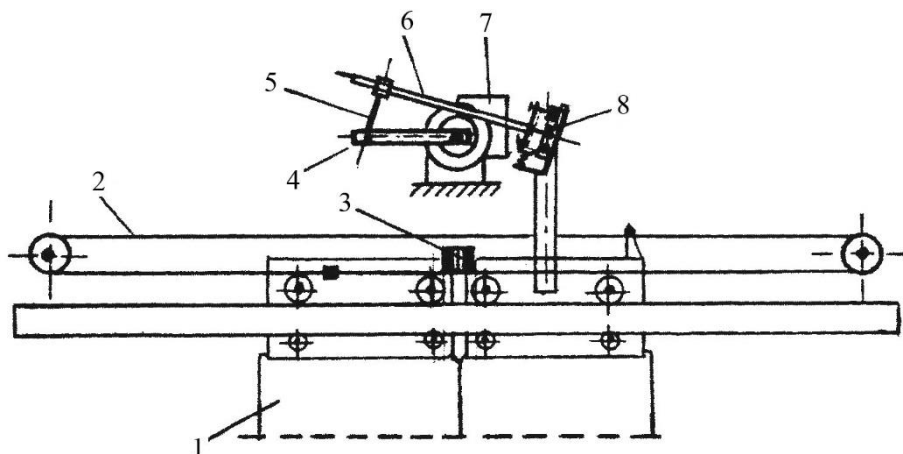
Схема механизма привода автоматических дверей штангового типа:
